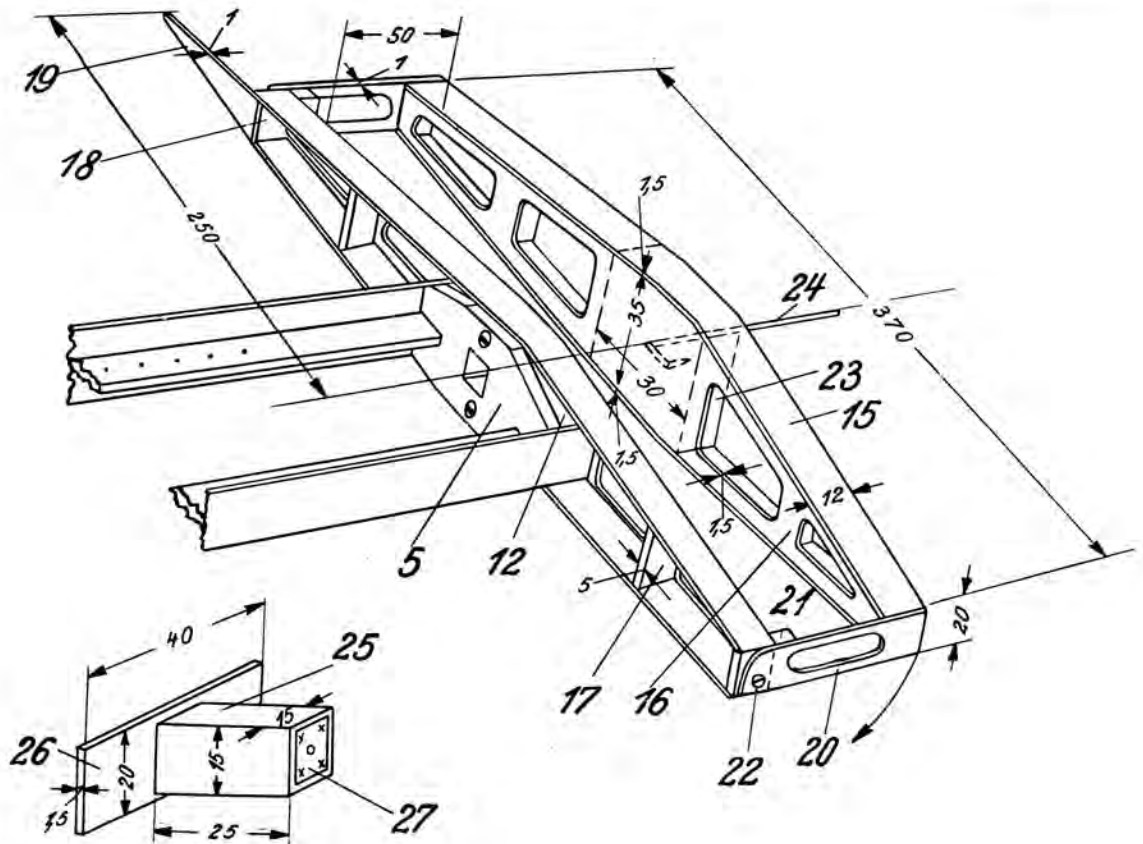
Der Querrahmen und das Luftschraubenlager.
